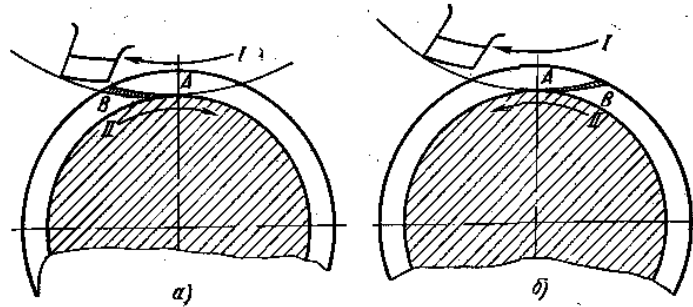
Виды фрезерования: а — встречное, б — попутное; I — направление вращения фрезы, II — направление вращения заготовки
